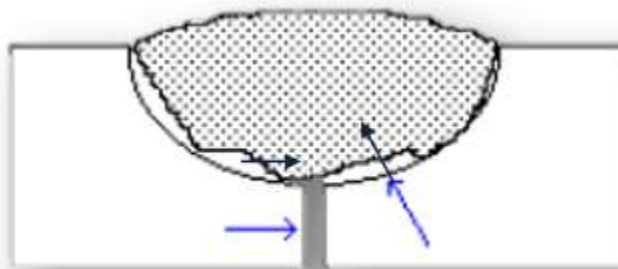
Defecto de penetración incompleta en soldadura
